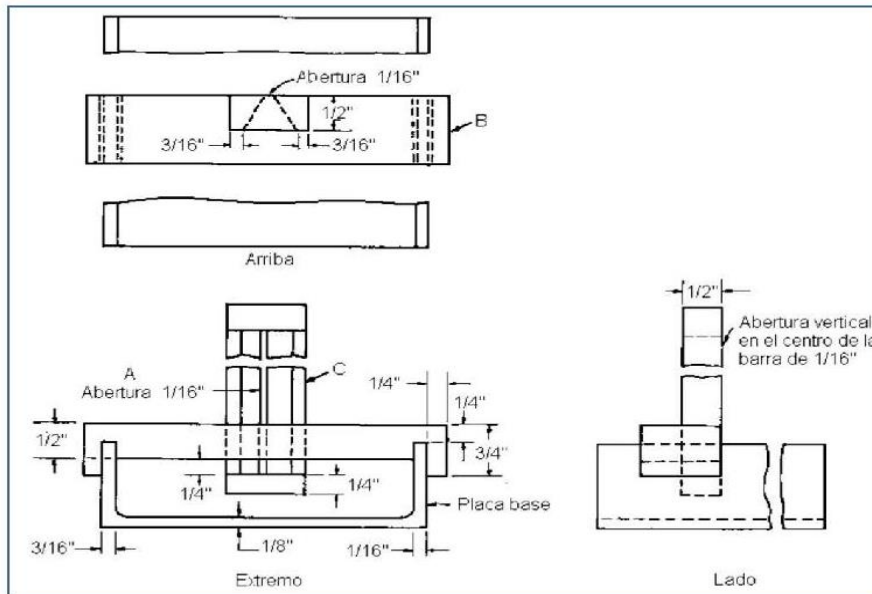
Detalle en planta del equipo adecuado para la determinación del diámetro final usado para el alineamiento del espécimen.
